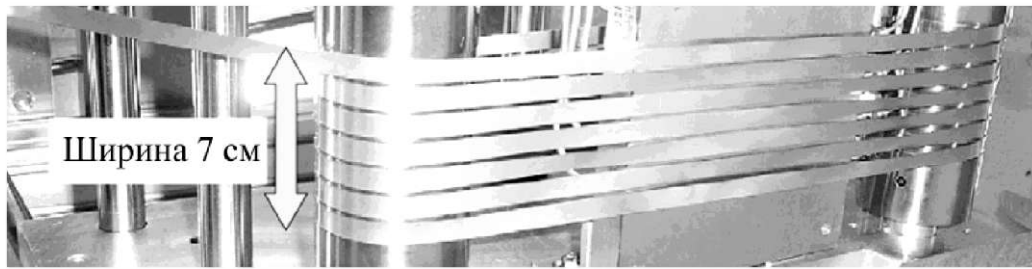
Розташування стрічки для багаторазового проходження крізь реактор (*SuperPower*, США)
